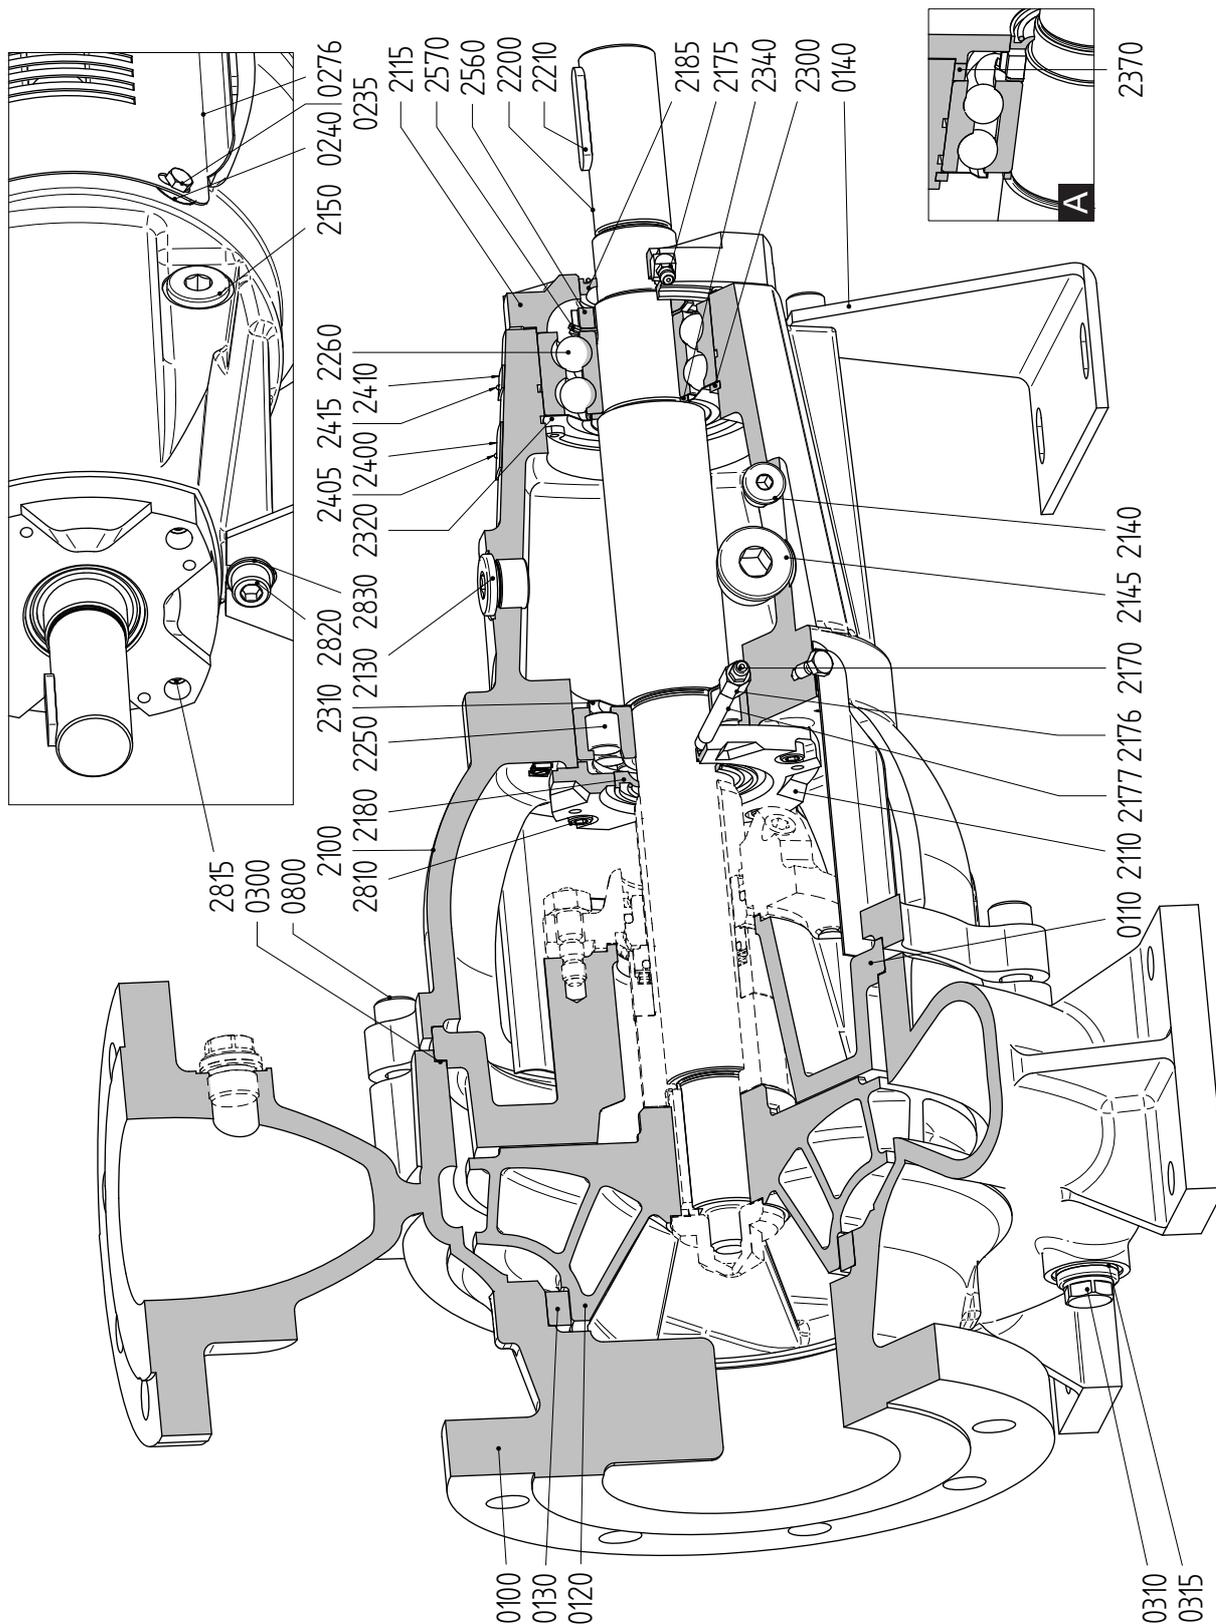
Чертеж в разрезе L2 с коническим отверстием (A = для группы подшипников 3)
